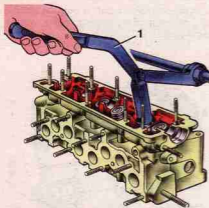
Сжатие пружин клапанов: 1 – приспособление 67.7823.9505
